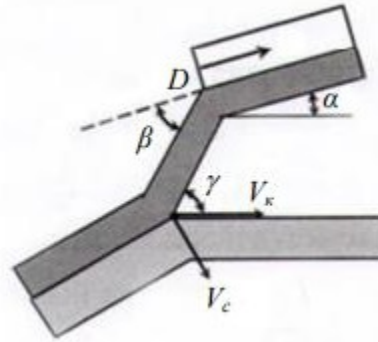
Кінематична схема зіткнення зварюваних пластин при зварюванні вибухом
